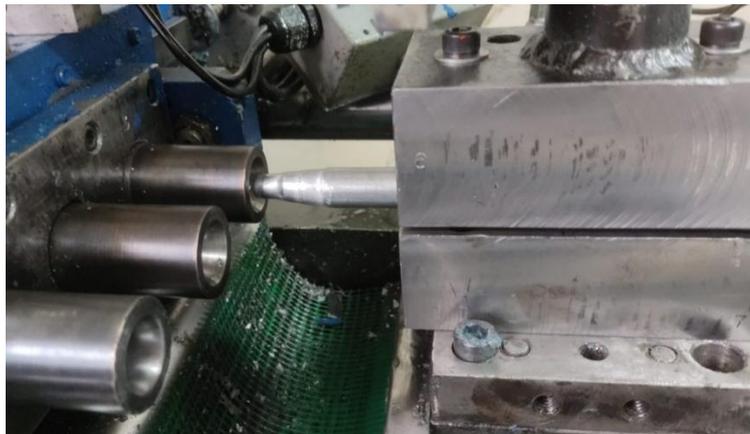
Abocinado extremo del tubo. Fuente: Autor.
